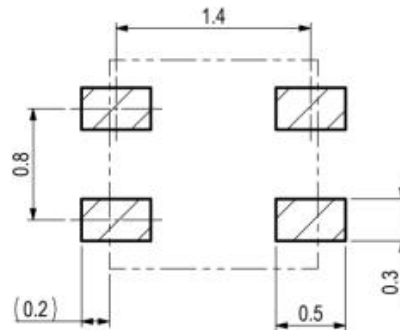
推荐传感器 PCB设计尺寸 (单位: mm)
